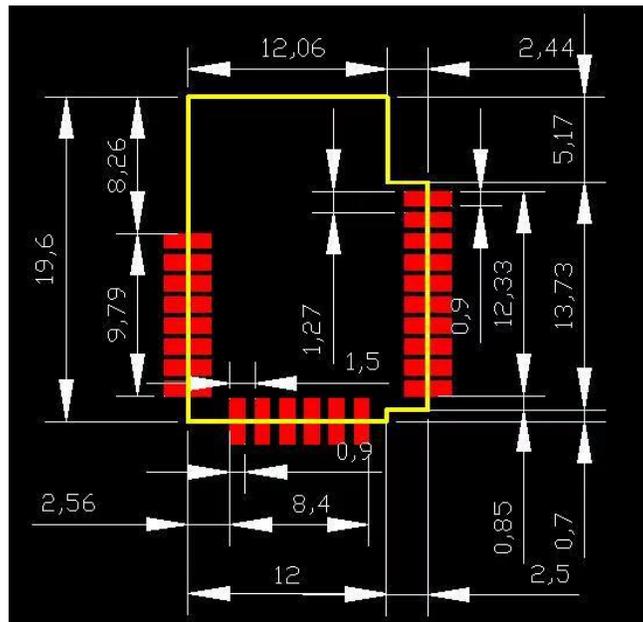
物理尺寸及推荐占地面积(单位:mm, 偏差:0.02mm)
